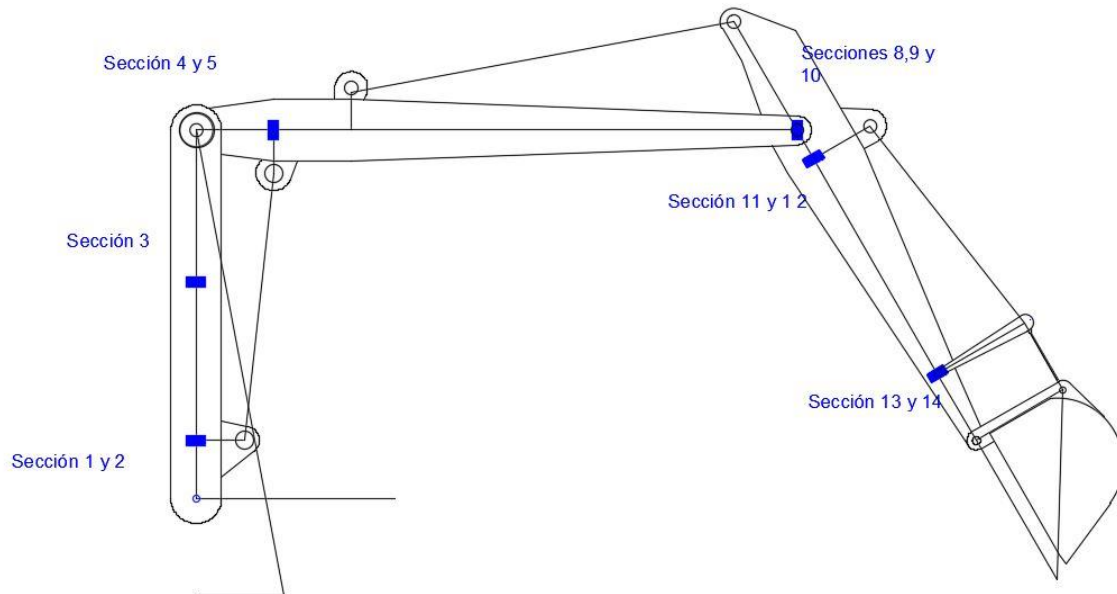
Croquis secciones sobre las que se medirán los esfuerzos internos
